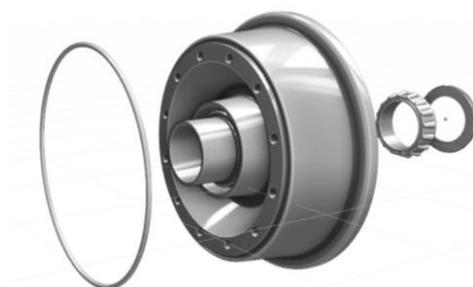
Извлечение стопорного кольца, сальника и подшипника из второй половины барабана колеса
